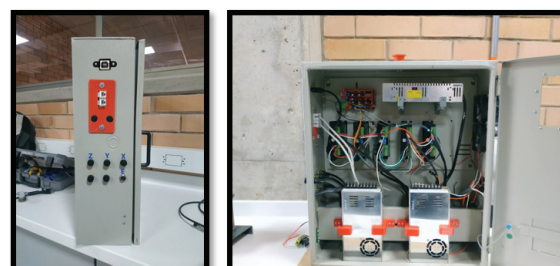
A) Vista frontal del controlador de la impresora 3D. b) Vista lateral del controlador de la impresora 3D. Fuente: Autor
